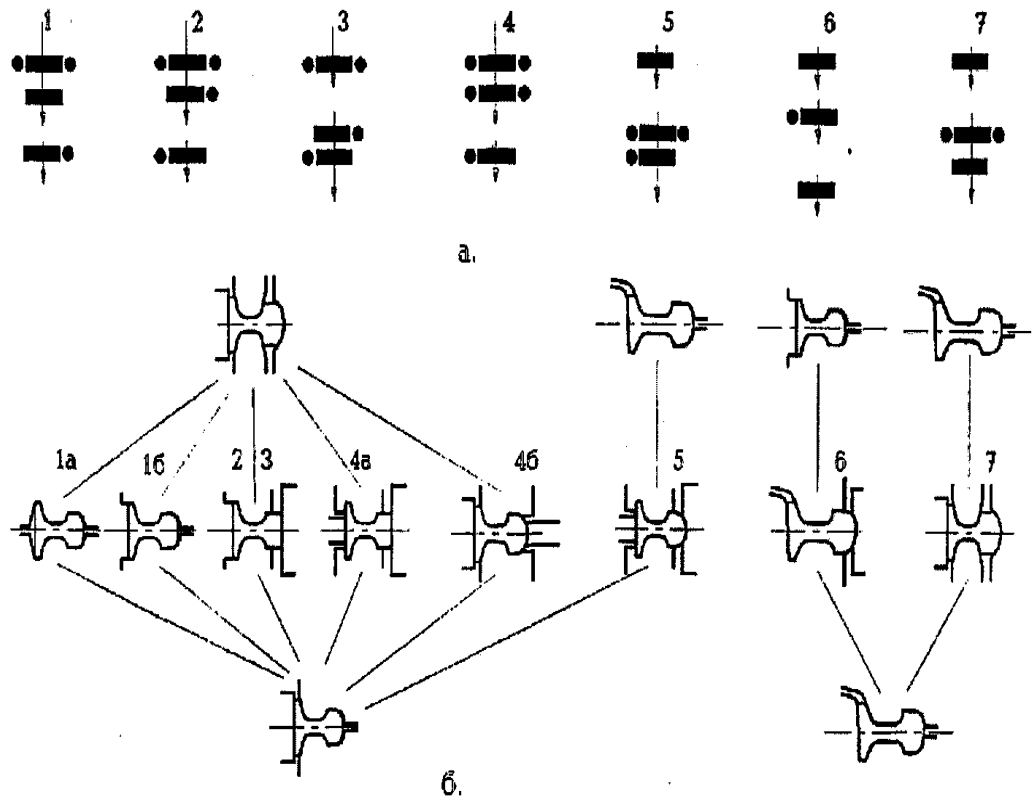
а) схема размещения рабочих клеток; б) способы прокатки в калибрах; 1-7 - номера способов прокатки.
